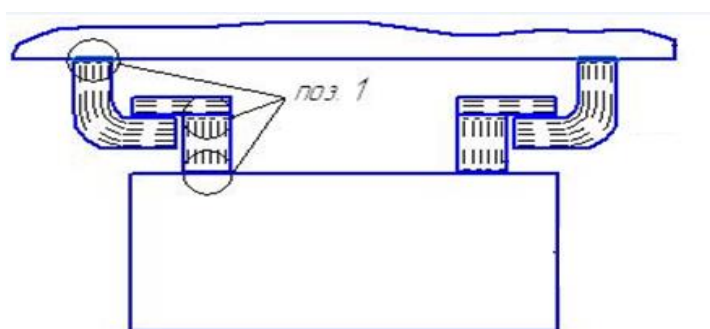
Контроль сварных соединений и околошовных зон кронштейна крепления бака-накопителя ЭЧТК и ЭЧТВ
